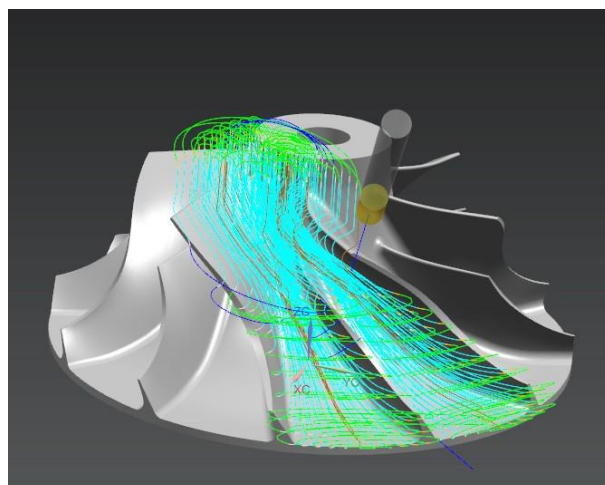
叶轮叶片 1 粗加工刀路轨迹
